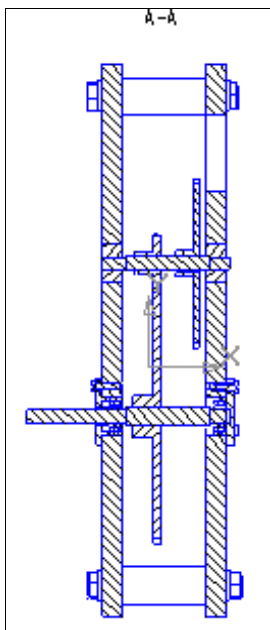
Разрез A-A, созданный с модели Редуктор
